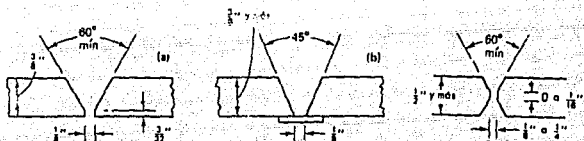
Juntas tope tipo "V": A) para oxiacetileno en acero; B) para arco eléctrico en acero; junta a tope "doble V" para soldadura de arco en acero.
